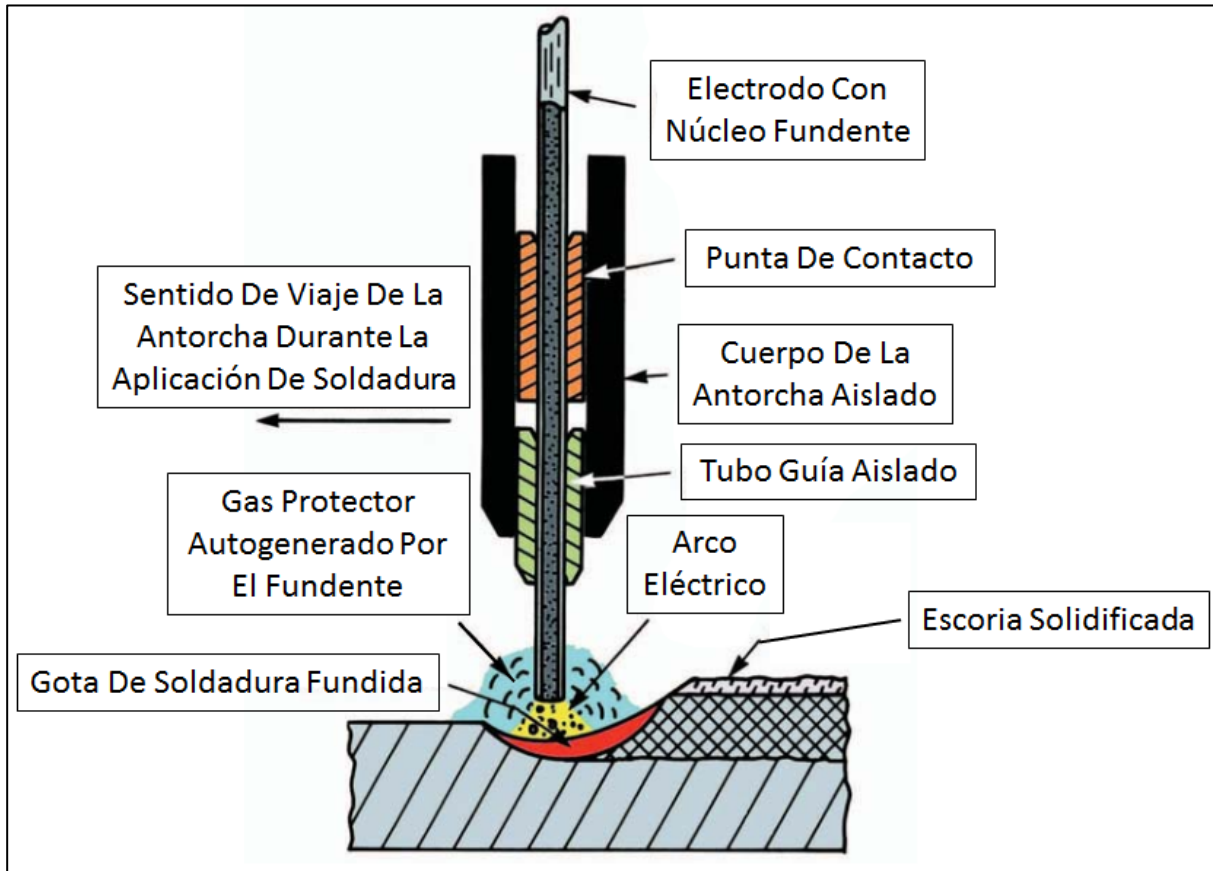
Proceso De Soldadura FCAW Autoprotegido [10].
